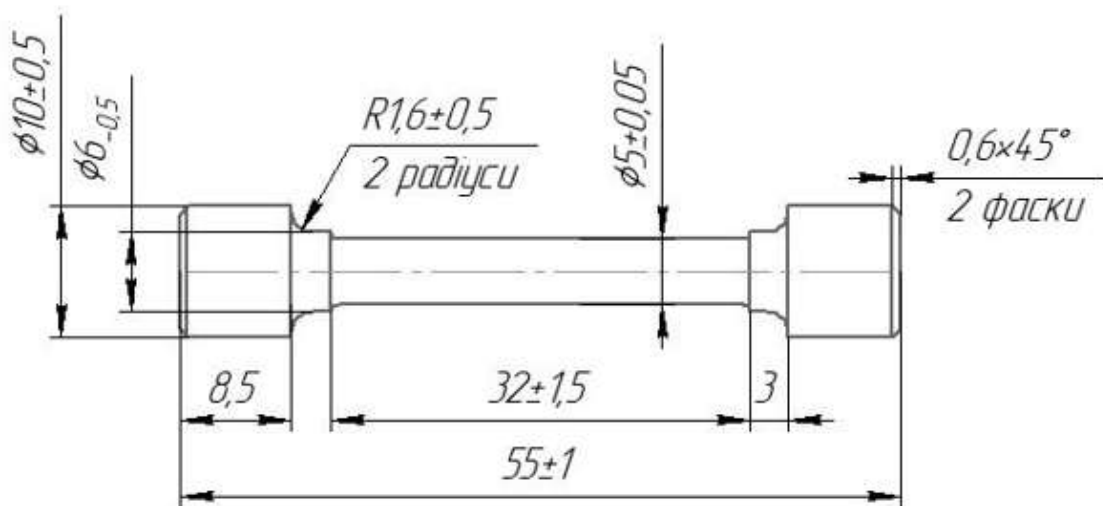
Циліндричний зразок для механічних випробувань
